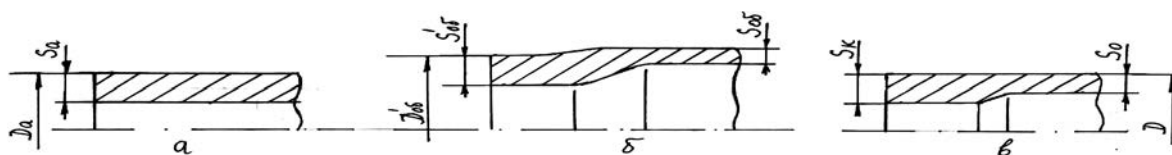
Схема формоизменения трубы в процессе прокатки с переменной по длине толщиной стенки: а - на автоматстане или стане «тандем»; б - на обкатной машине; в - на калибровочном стане
